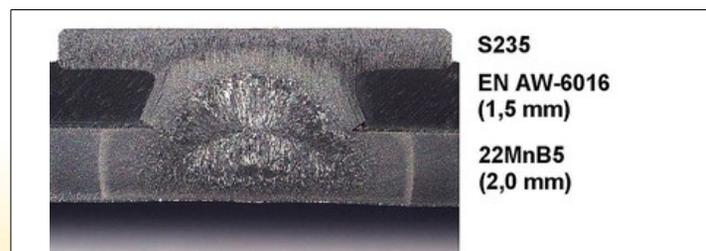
soudage par résistance avec élément de l'aluminium sur acier (source: Laboratory of Materials and Joining Technology, l'université de Paderborn)
